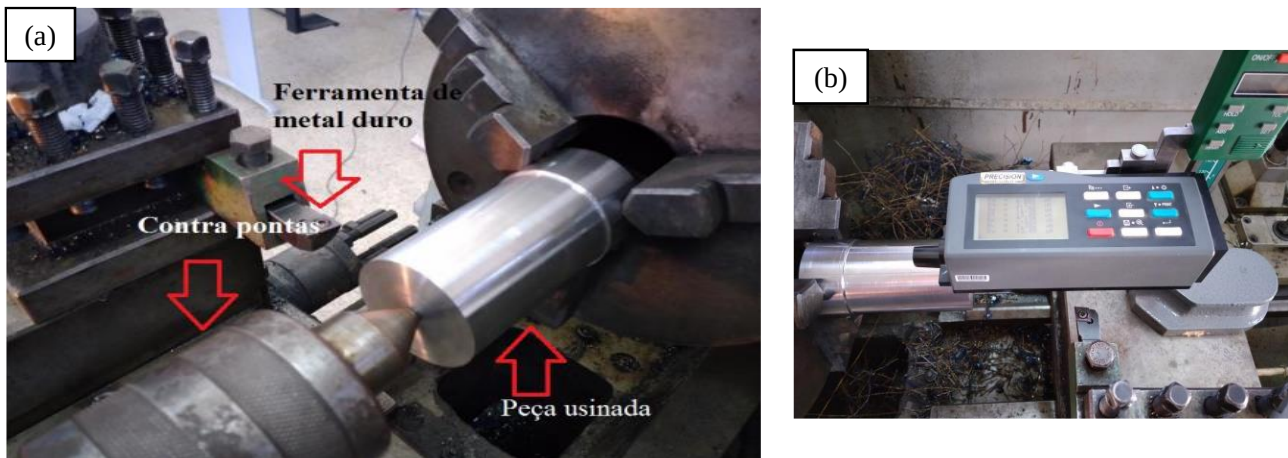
(a) Detalhe da montagem da máquina-ferramenta para os ensaios de torneamento cilíndrico externo. (b) Montagem para realização das medições de rugosidade.
